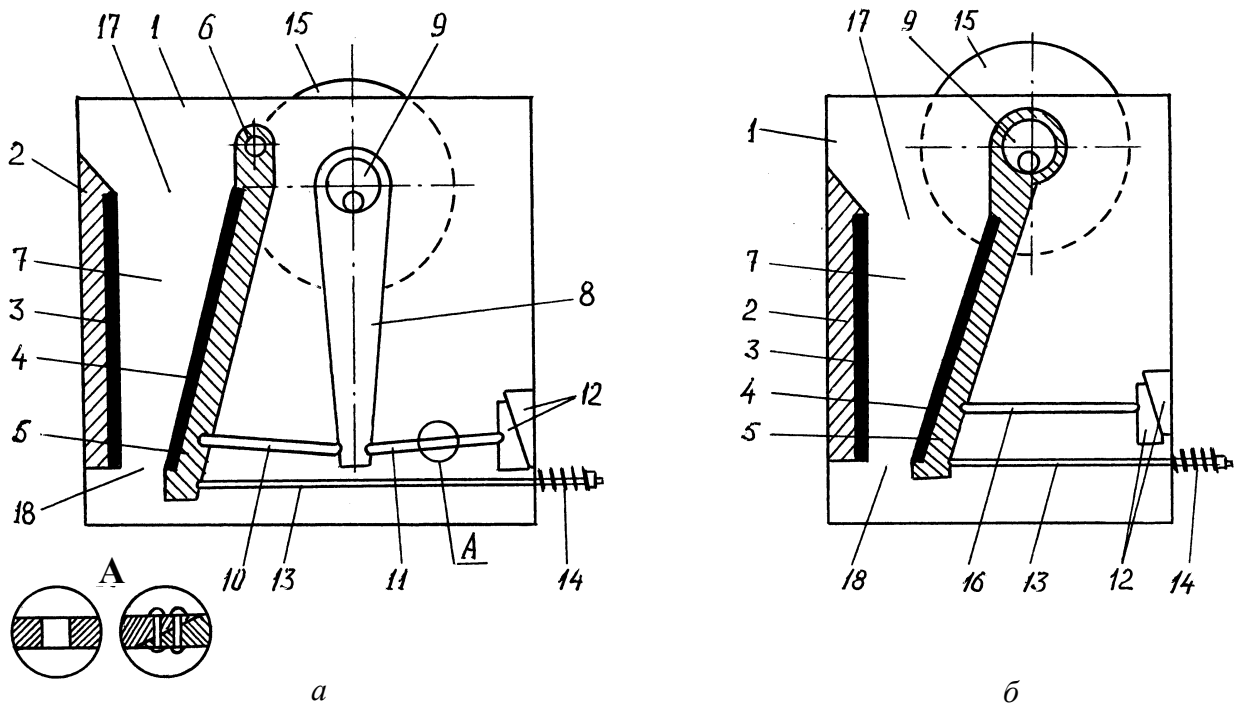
Виконання щоків дробарок: *а* – з простим рухом щоки; *б* – зі складним рухом щоки: 1 – корпус; 2 – нерухома щока; 3, 4 – броньові плити; 5 – рухома щока; 6 – вісь підвісу рухомої щоки; 7 – камера дроблення; 8 – шатун; 9 – ексцентриковий вал; 10 – передня розпірна плита; 11 – задня розпірна труба; 12 – регульовальні клини; 13 – тяга; 14 – пружина; 15 – маховик; 16 – розпірна плита; 17 – завантажувальний отвір (паца, зів); 18 – розвантажувальний отвір (шпальт)
